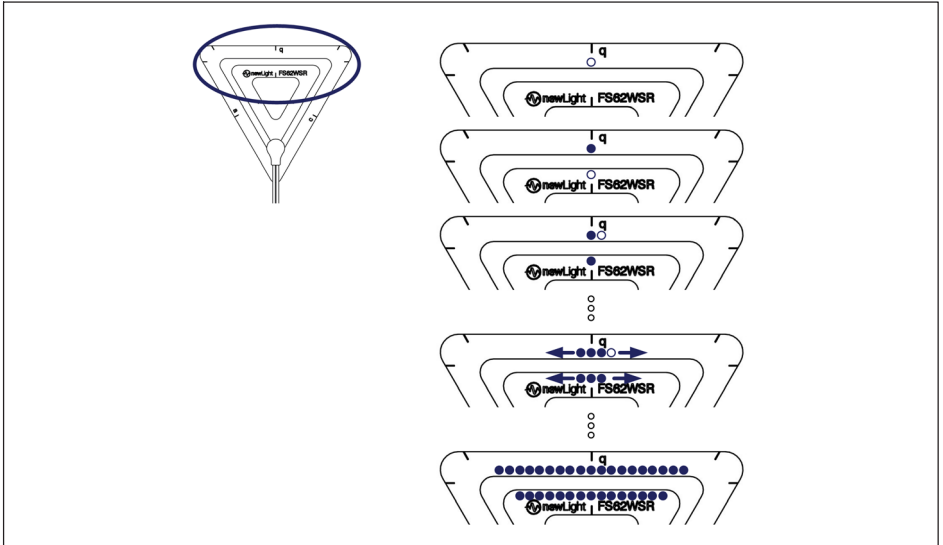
Anschweißverfahren der Rosette FS62WSR BRD in jeder Messrichtung
